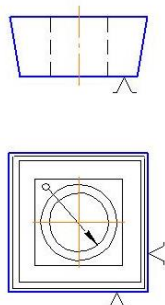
Схема базирования и закрепления сменных пластин.
